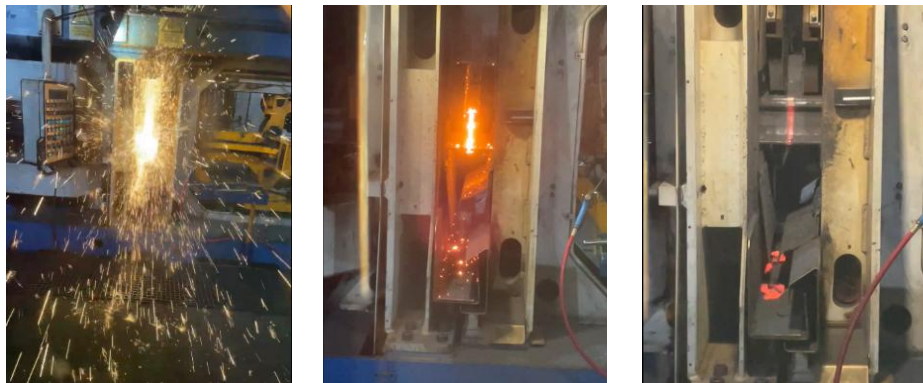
Fases de un proceso de soldadura. Fuente: Propia
